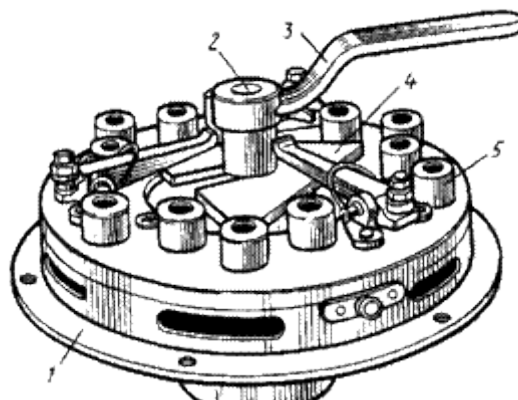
Стенд для разборки и сборки муфты сцепления:
